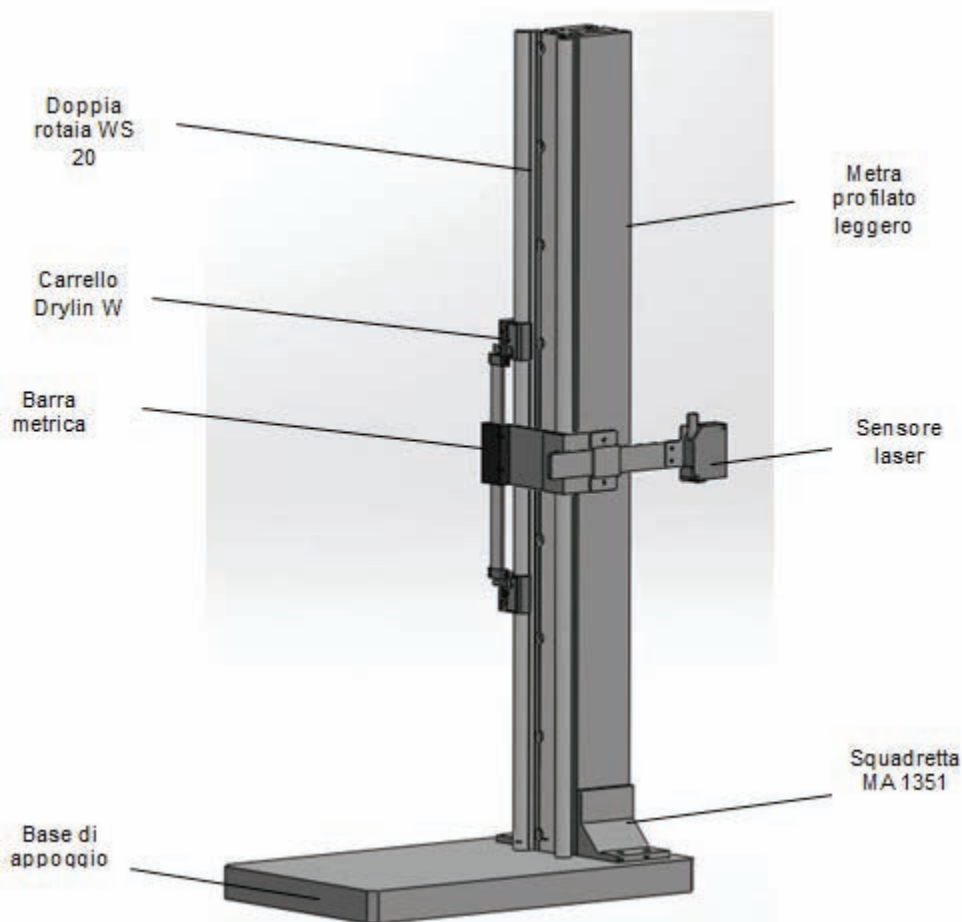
Insieme del supporto per il sensore laser e per la barra metrica
